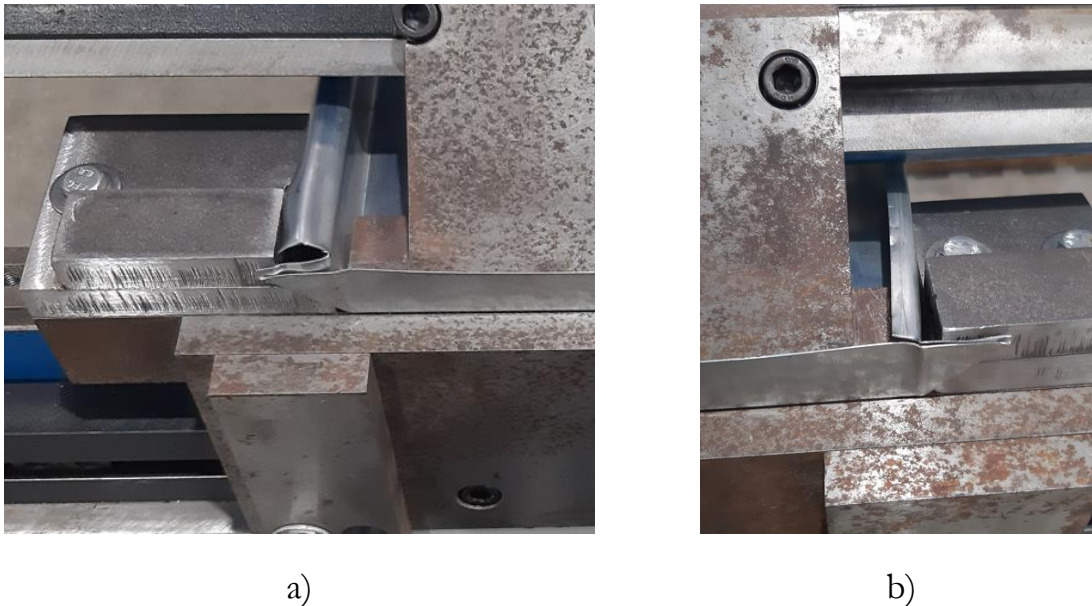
Teste de quinagem a 90 graus: a) lado 1; b) lado 2
